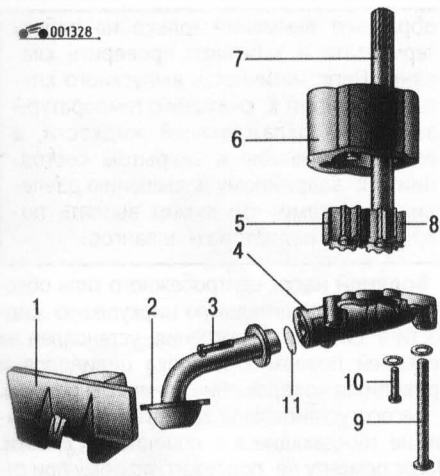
Масляный насос четырехцилиндрового двигателя: 1 – перегородка; 2 – маслоприемник; 3 – болт крепления маслоприемника; 4 – крышка масляного насоса; 5 – ведомая шестерня; 6 – корпус масляного насоса; 7 – вал привода масляного насоса; 8 – ведущая шестерня; 9 – болт крепления масляного насоса; 10 – болт крепления крышки масляного насоса; 11 – уплотнительное кольцо маслоприемника
